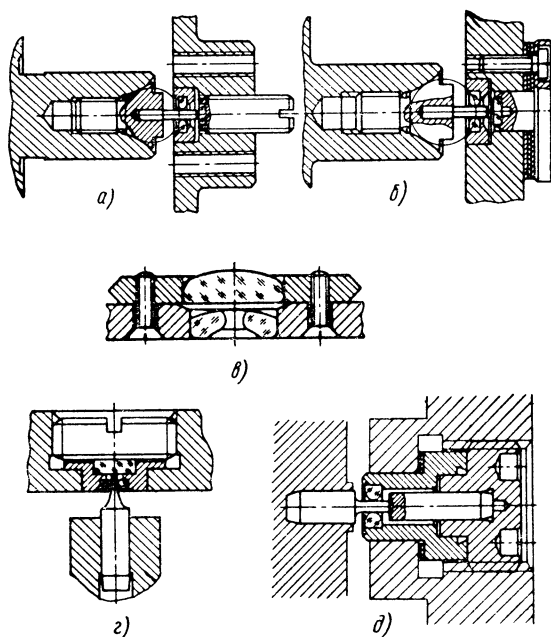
Разборные конструкции цилиндрических закрытых опор
